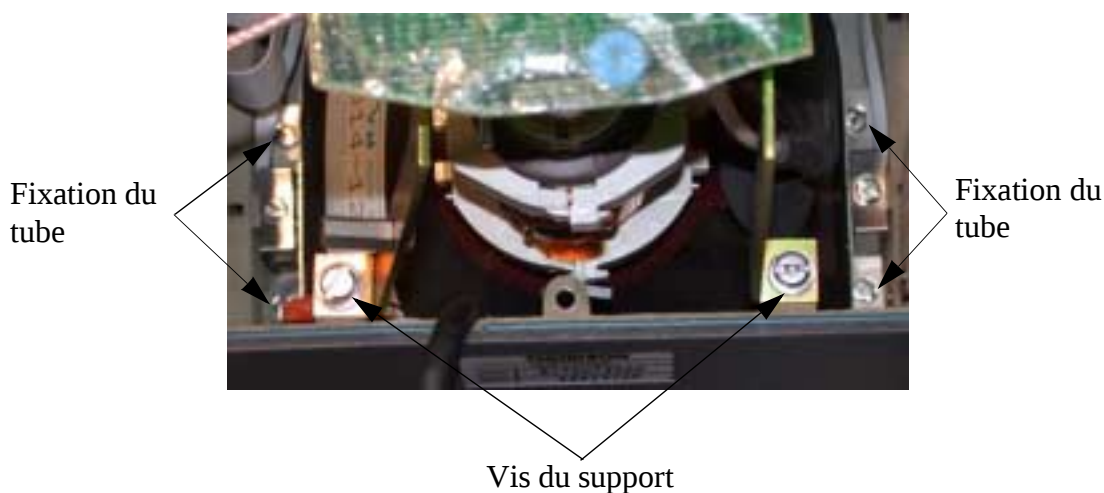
Fixation du support de la carte SWEEP BOARD et du tube
